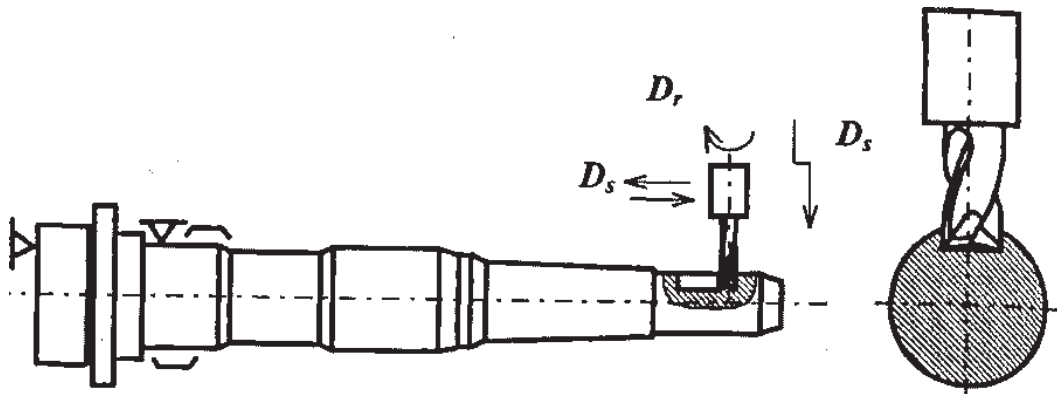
Схема фрезерования шпоночного паза под призматическую шпонку на шпоночно-фрезерном станке
